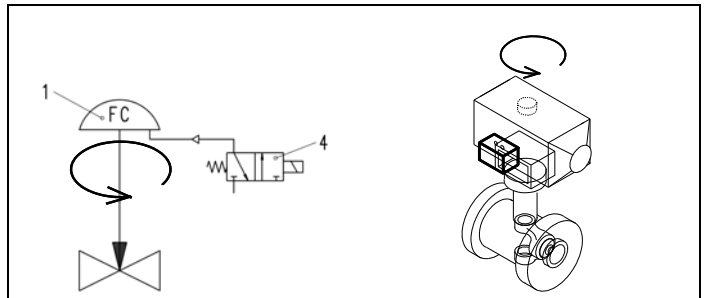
Wirkbild bei Ausführung mit Magnetventil – die Sicherheitsstellung ist – Ventil zu – Die Feder hält die Armatur geschlossen
